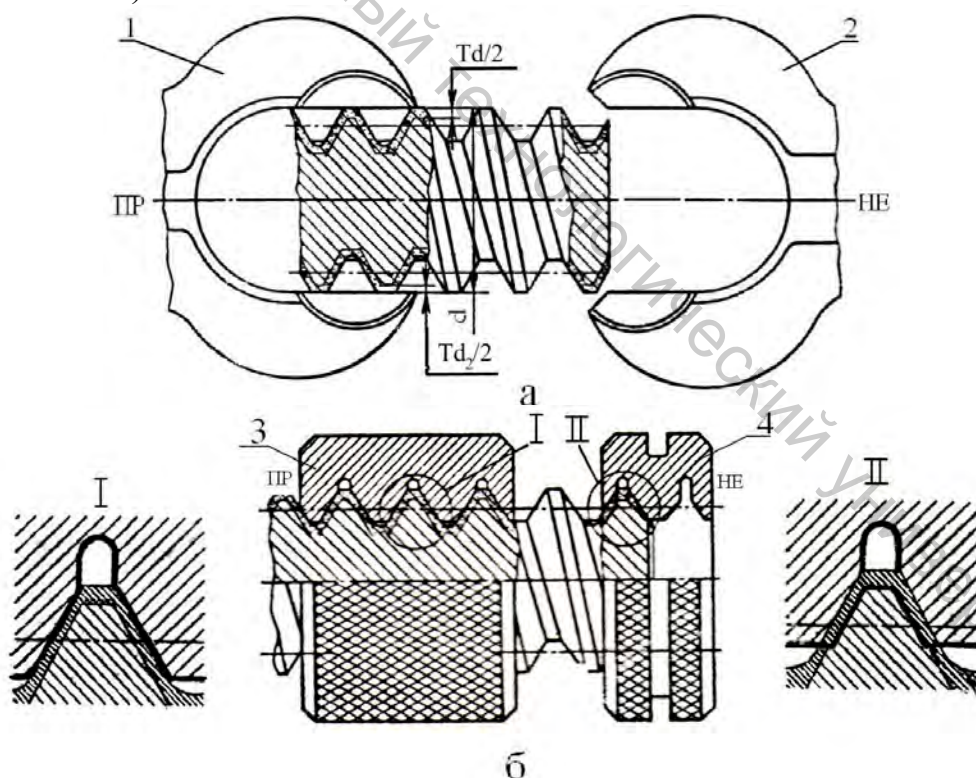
Схемы контроля калибрами допусков наружной резьбы:
